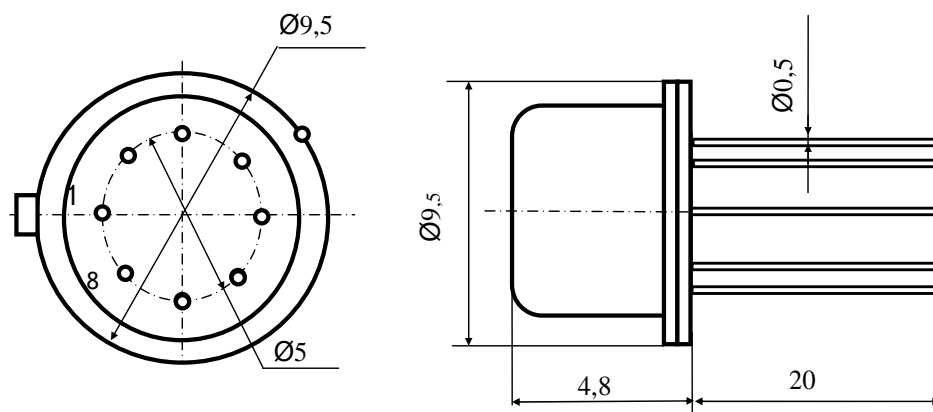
Внешний вид и габаритные размеры аналоговой микросхемы в корпусе 301.8-2
